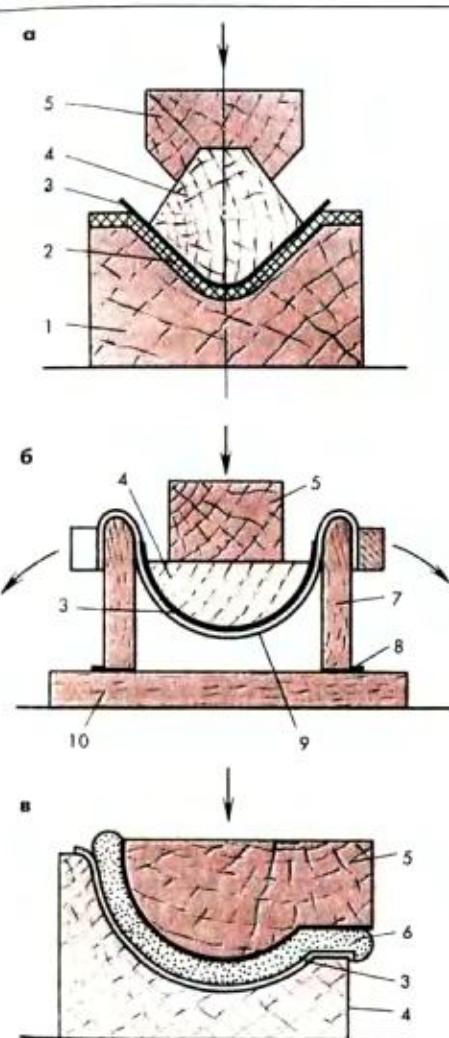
Облицовывание криволинейных поверхностей в приспособлениях: а – с жесткой цулагой; б – с гибкой лентой; в – с сыпучей цулагой; 1 – жесткая цулага, 2 – прокладка; 3 – облицовка; 4 – облицовываемая заготовка; 5 – прижимные бруски; 6 – сыпучая цулага; 7 – откидные бруски; 8 – петли; 9 – лента; 10 – основание
